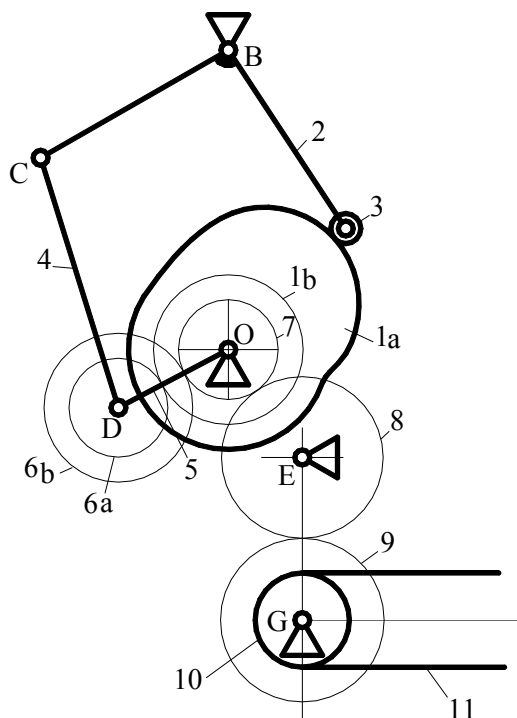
Зубчато-кулачковый дифференциальный механизм транспортёра
